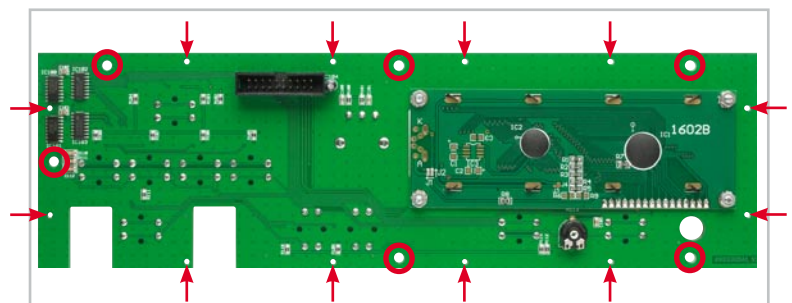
Die Lage der Befestigungsbohrungen und der Bohrungen für die Führungsstifte des Frontrahmens auf der Frontplatine
